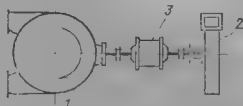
Схема сборки валковой среднеходной мельницы типа МВС-140 с мельничным вентилятором:
